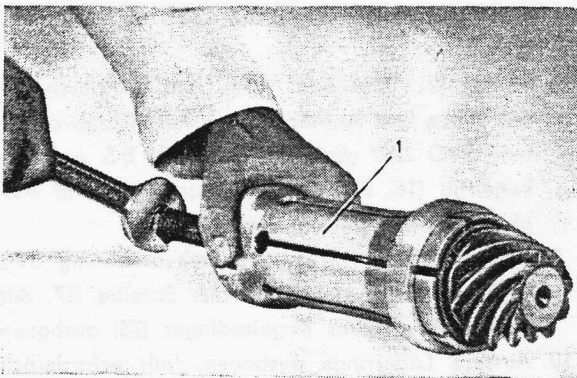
Ausbau des hinteren Antriebskegelradlagers
